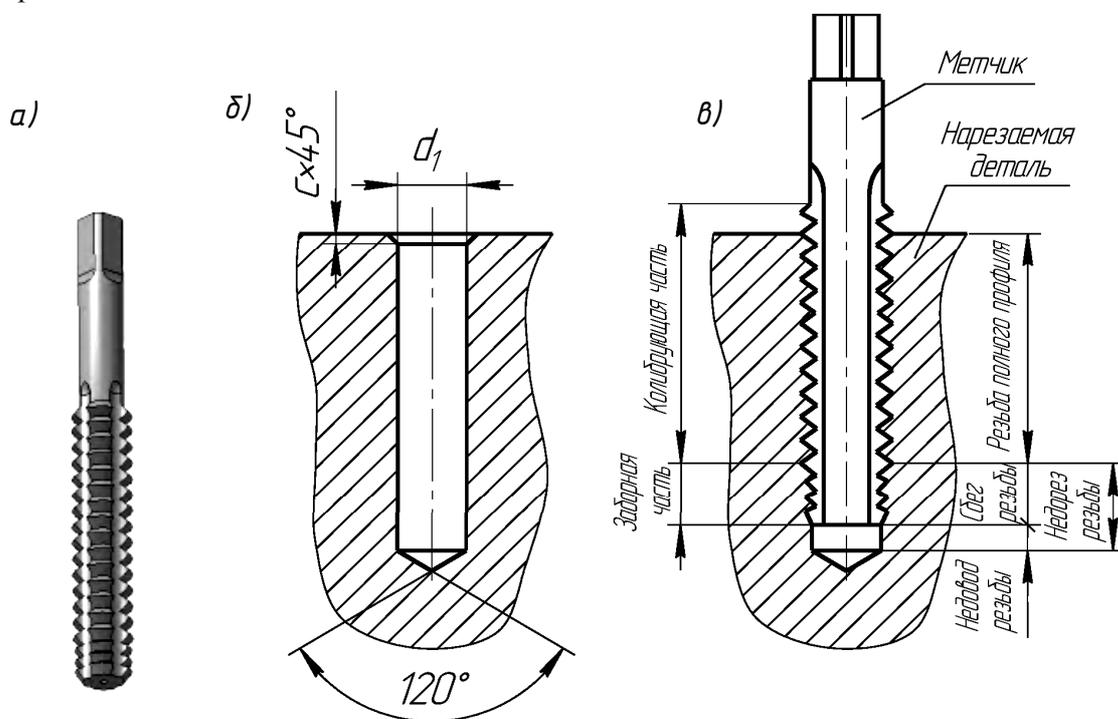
Нарезание внутренней цилиндрической резьбы:
